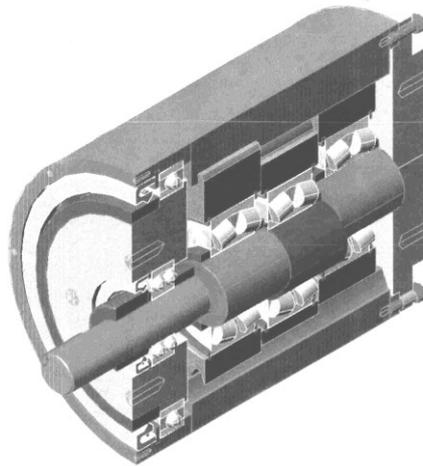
Эпициклический планетарный редуктор с кулачкообразным валом
